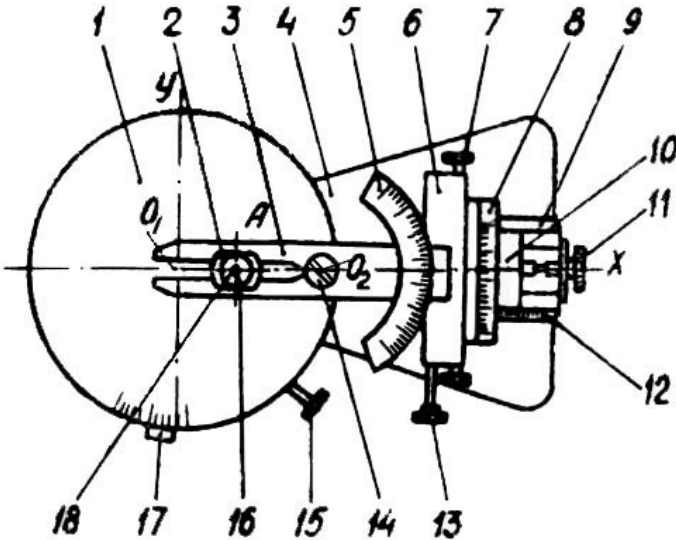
Установка ТММ-21 для моделювання кулачкових механізмів
